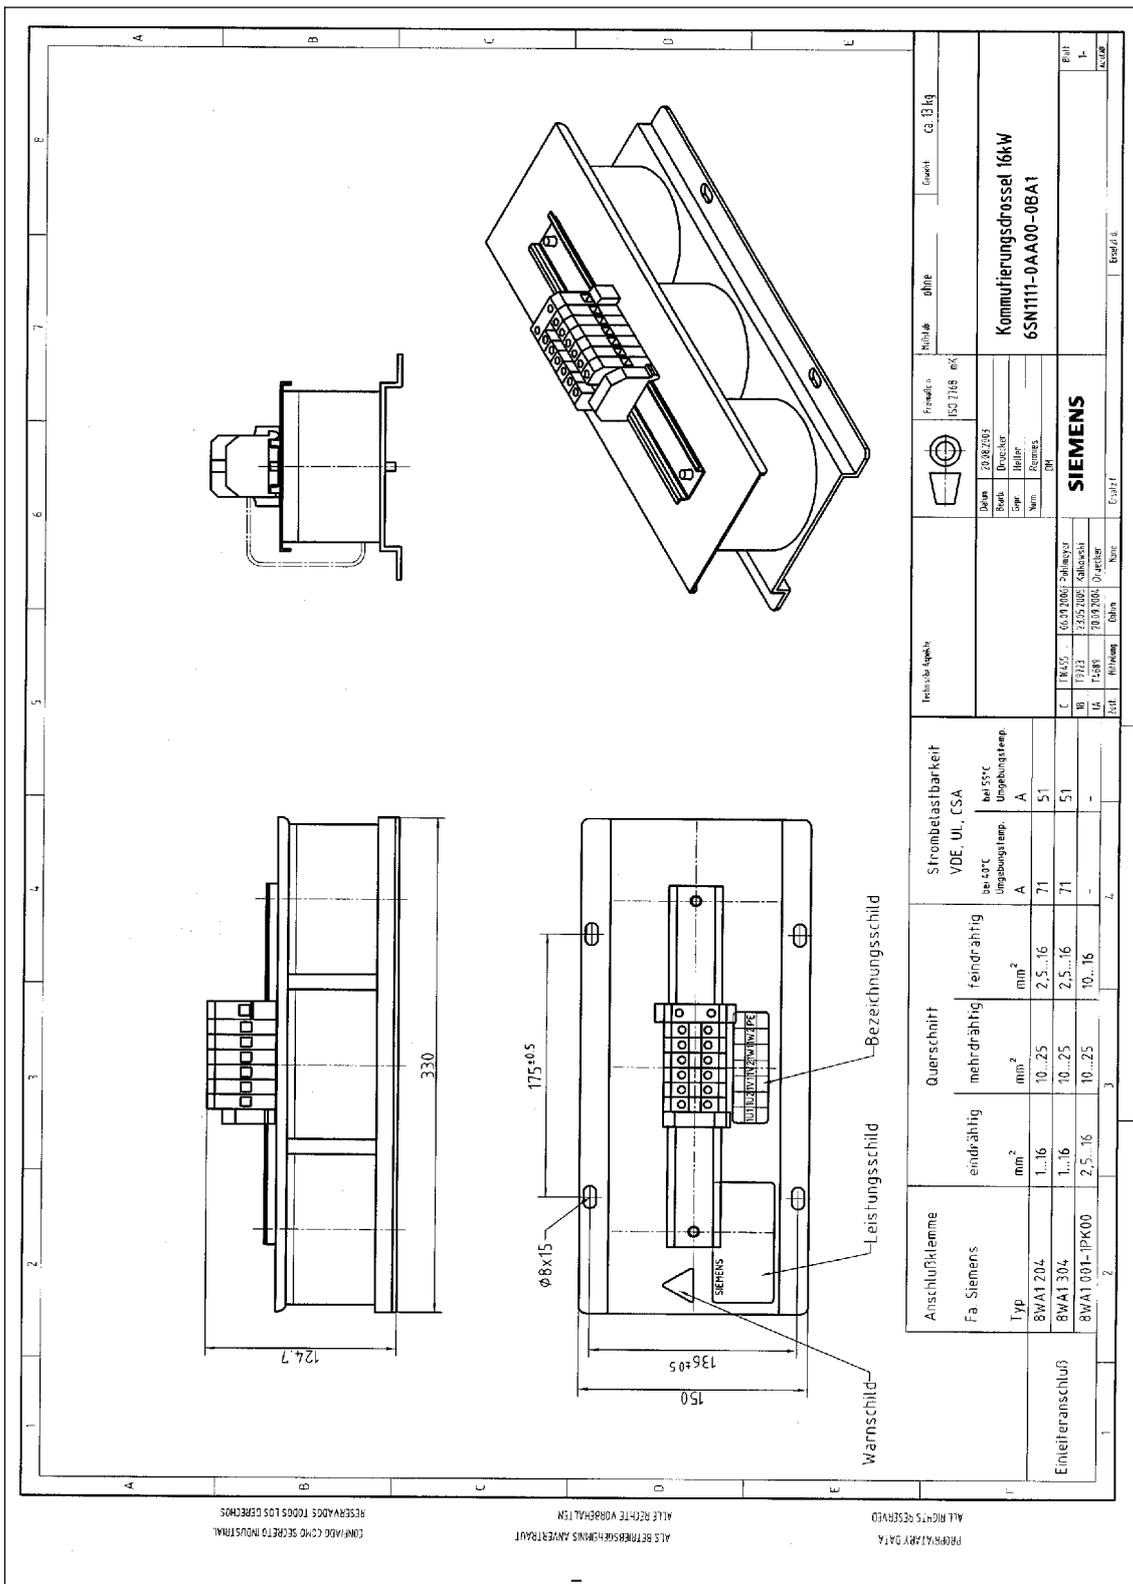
Bobina HF trifásica 16 kW, 6SN1111-0AA00-0BAx
